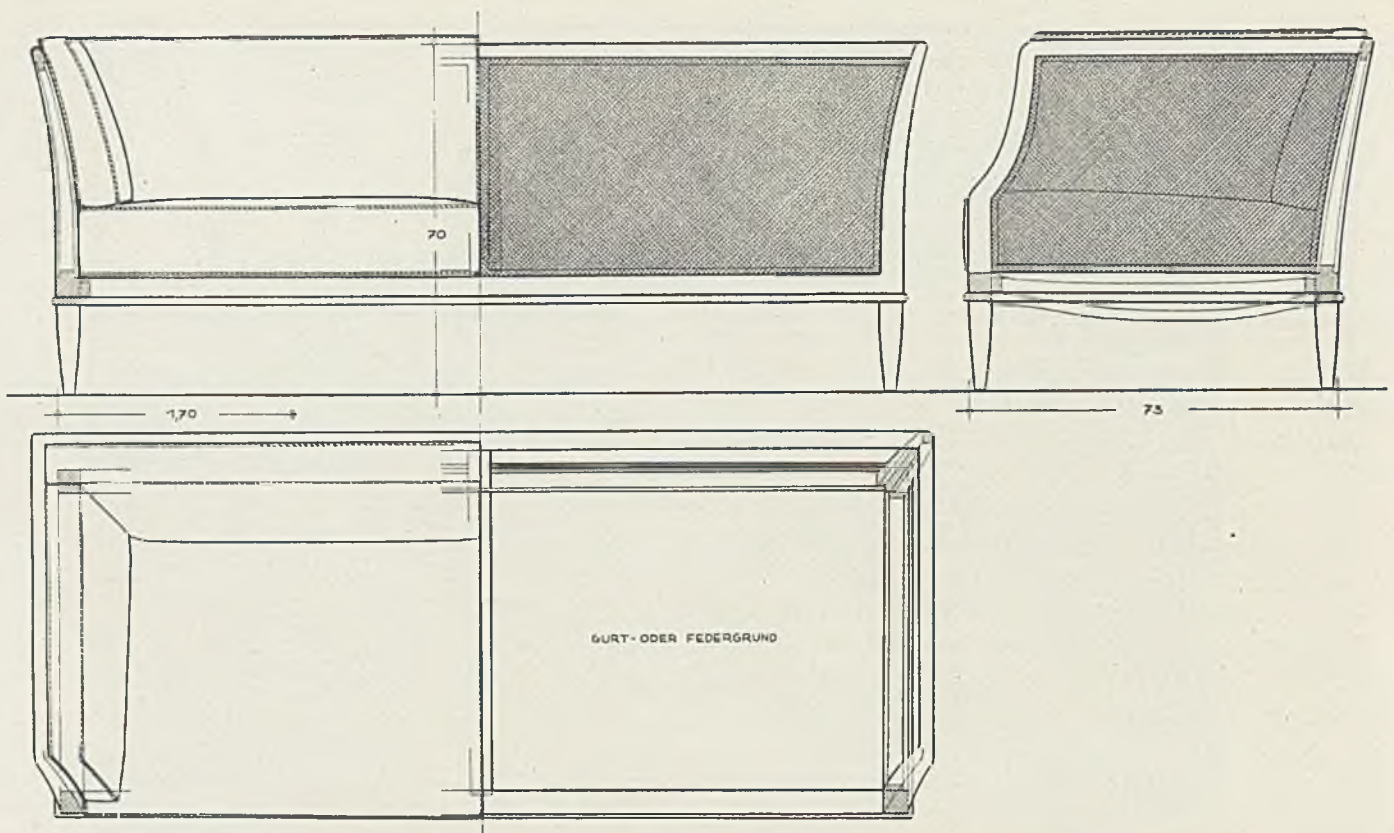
Werkzeichnung zur Sofabank mit losen Kissen. Das leichte Holzgestell hat angeleimte oder angefräste Fälze, welche beidseitig mit Rohr ausgeflochten sind
